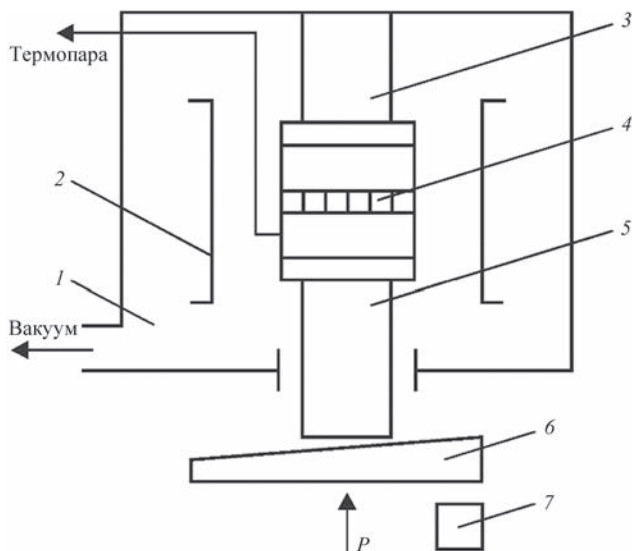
Схема робочої камери установки для дифузійного зварювання; 2 – нагрівач з молібдену; 3 – верхній шток; 4 – тришарова панель, поміщена в обмежувальну втулку; 5 – нижній шток; 6 – клин; 7 – прес
